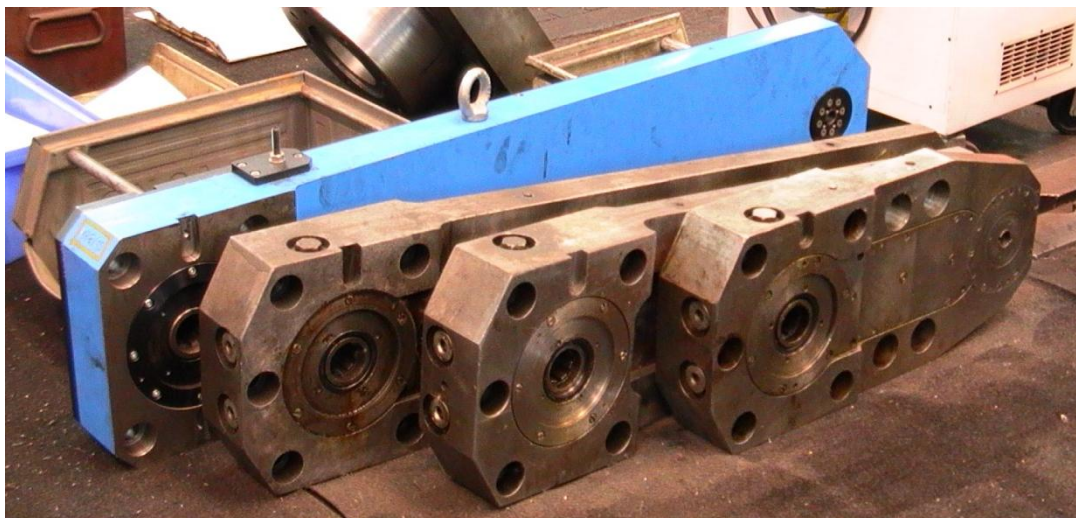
NC svrtávací zařízení pro velké rotory [12]
